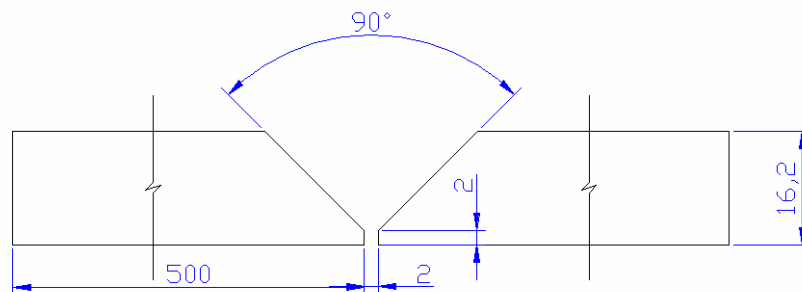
Representação esquemática da junta soldada [mm]
